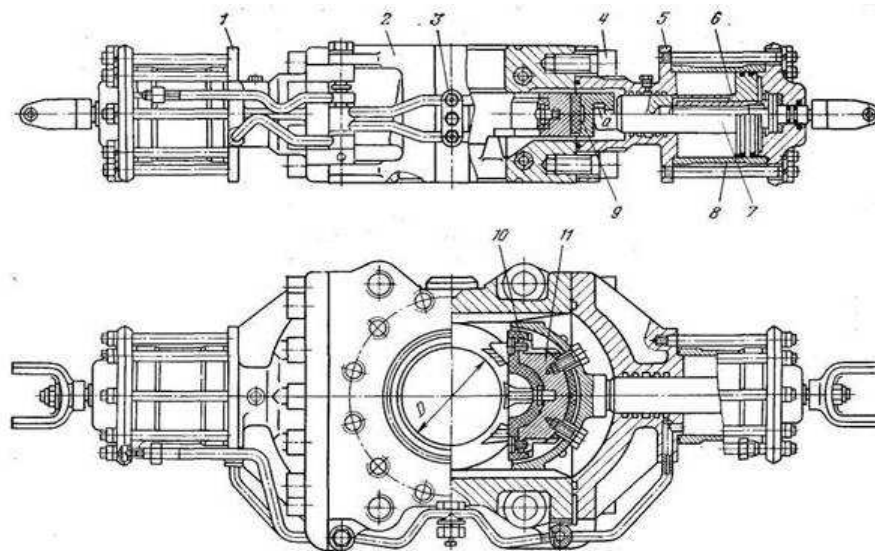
Плащечный превентор: 1-крышка; 2-корпус превентора; 3-коллектор; 4-болты; 5,8- гидроцилиндры; 6-поршень; 7-шток; 9-корпус плашки; 10-резиновое уплотнение; 11-сменные вкладыши
